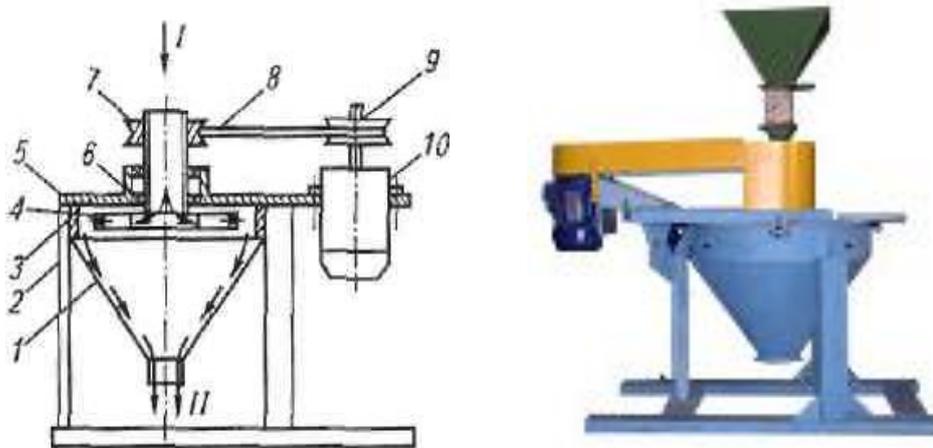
Схема центробежного шелушителя ЦШ-1
